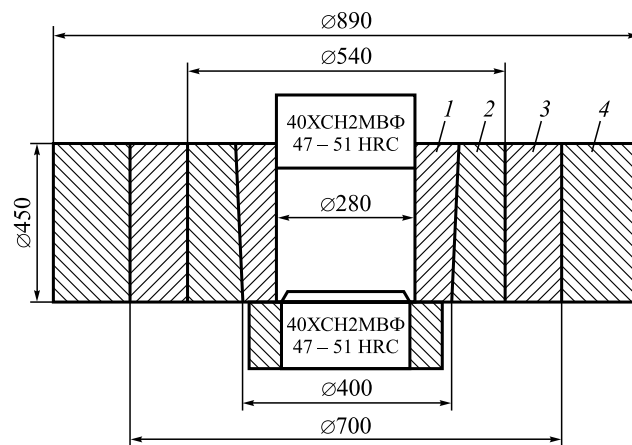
Схема камеры высокого давления с диаметром рабочей зоны 280 мм:
